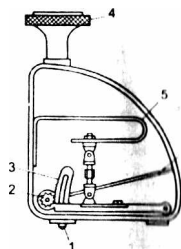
Твердомер Шора: 1 — игла; 2 — зубчатые колеса; 3 — зубчатый сектор; 4 — головка; 5 — пружина; 6 — стрелка прибора
